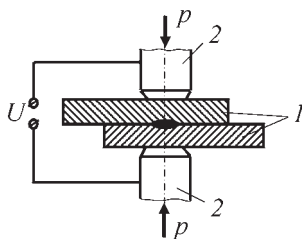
Схема точечной электроконтактной сварки:
